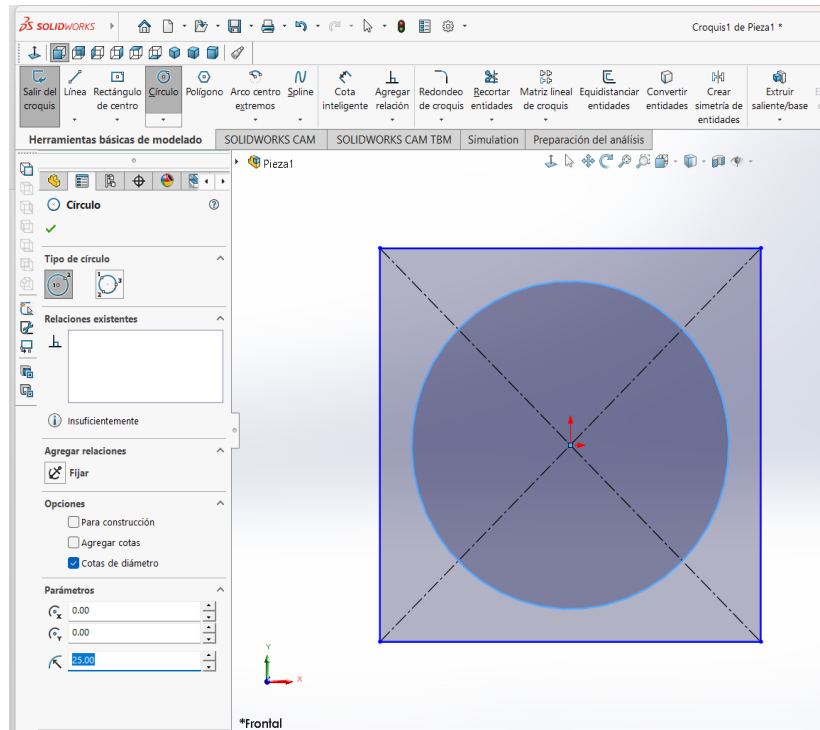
Croquis 2 Corte avanzado. Fuente: Creación propia
